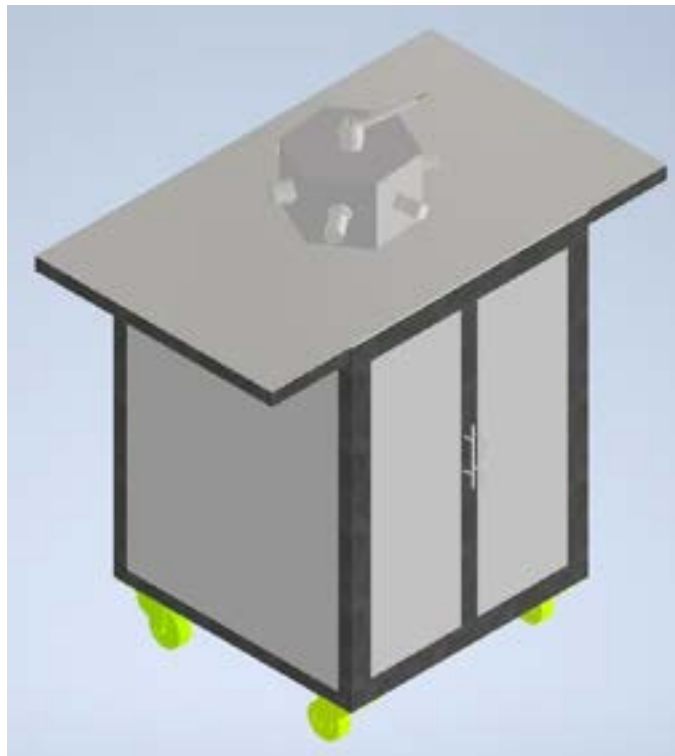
Módulo de montaje y desmontaje de rodamientos.
